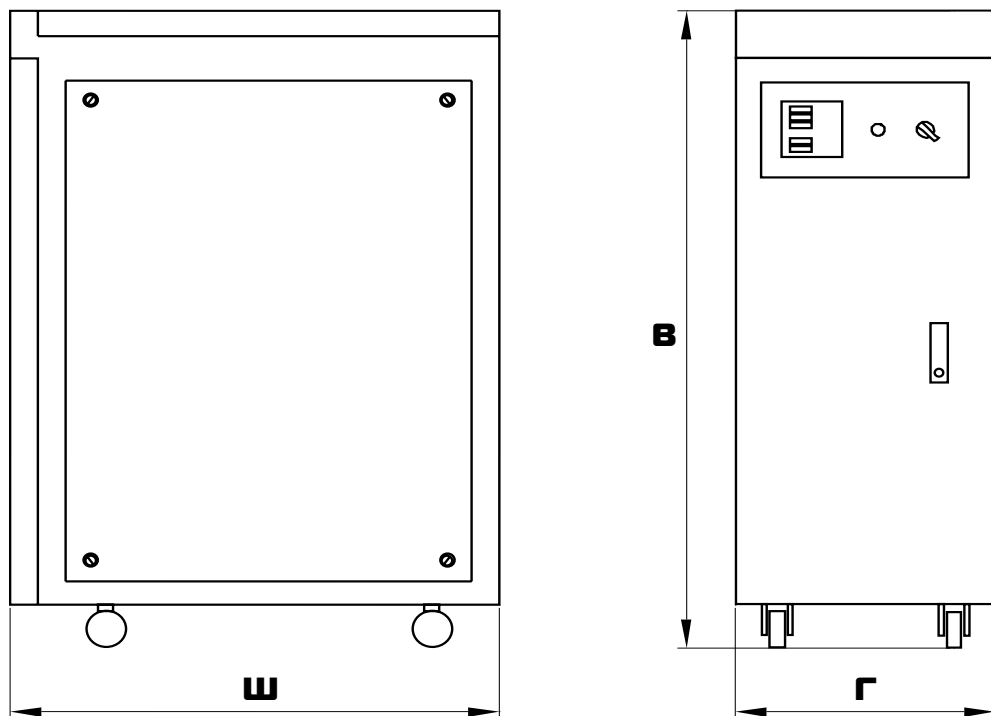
Габаритный чертеж трехфазного СТЭМ-2 IP31 30-200 кВА
